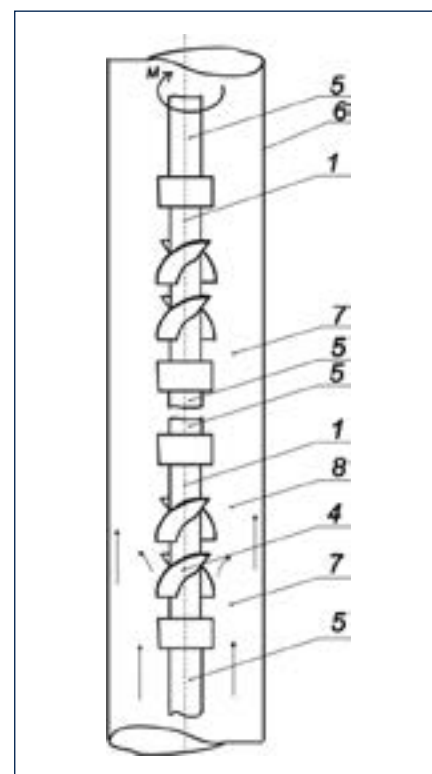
Компоновка колонны штанг со штанговыми лопатками в НКТ
